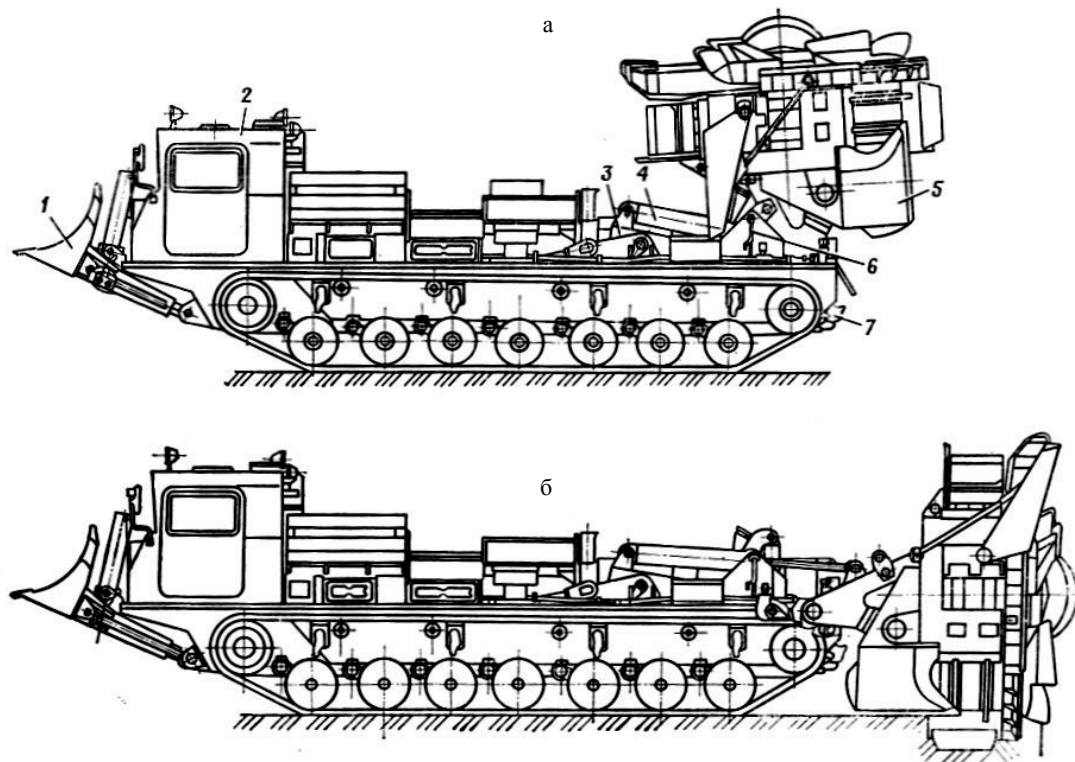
Котлованная машина МДК-3 (компоновочная схема): а – транспортное положение; б – рабочее положение; 1 – бульдозерное оборудование; 2 – базовая машина; 3 – рама; 4 – гидроцилиндр поворота; 5 – рабочий орган; 6 – фиксатор рабочего органа; 7 – рыхлительное оборудование
